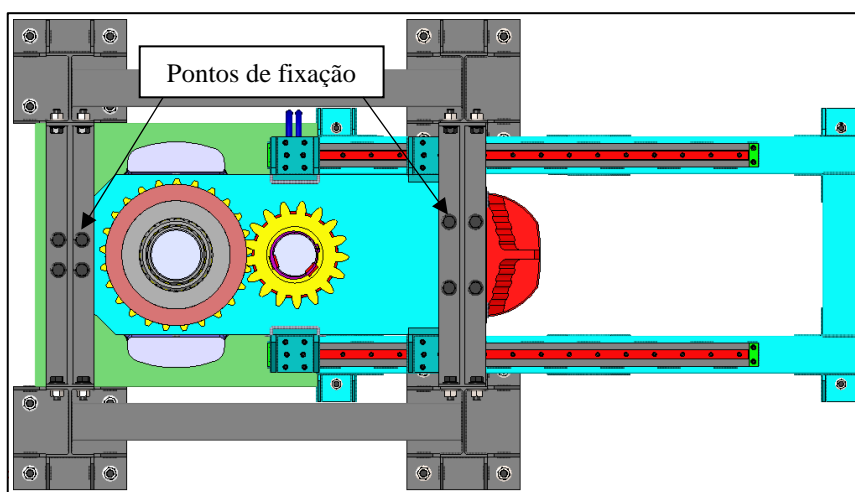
Representação esquemática em vista em corte transversal da vista superior do equipamento destacando os pontos de fixação da estrutura
